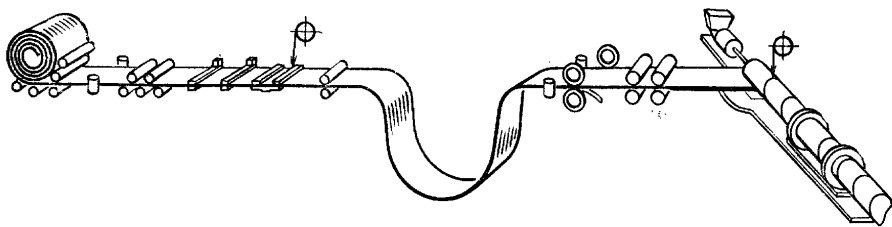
Схема стана для изготовления труб из ленты спиральным швом
